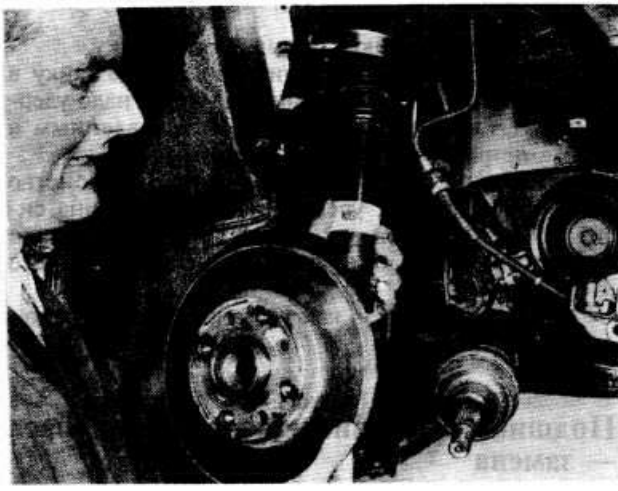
Извлечение сборки стойка подвески/опора ступицы
